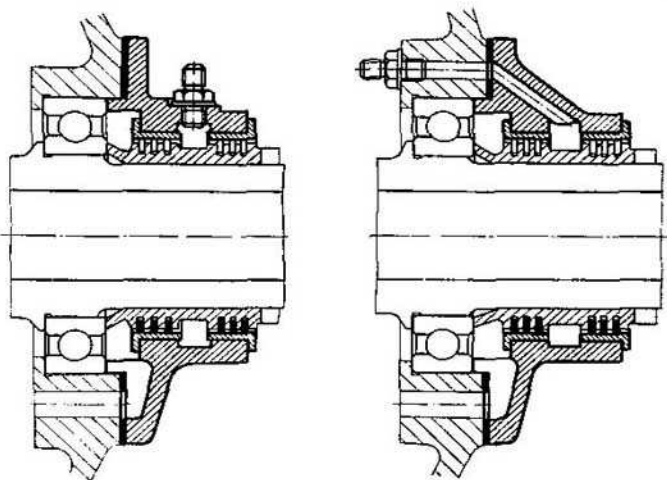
Empaquetadura sopladora de un cojinete de contacto rodante
